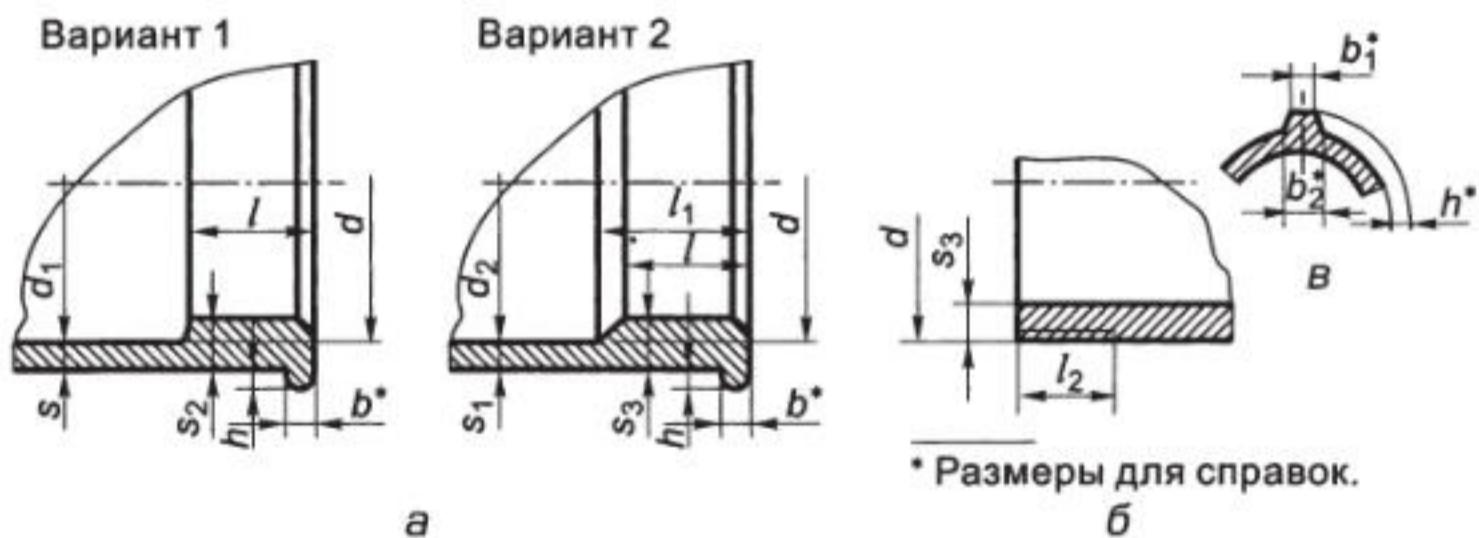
Размеры конструктивных элементов соединительных частей трубопроводов:
